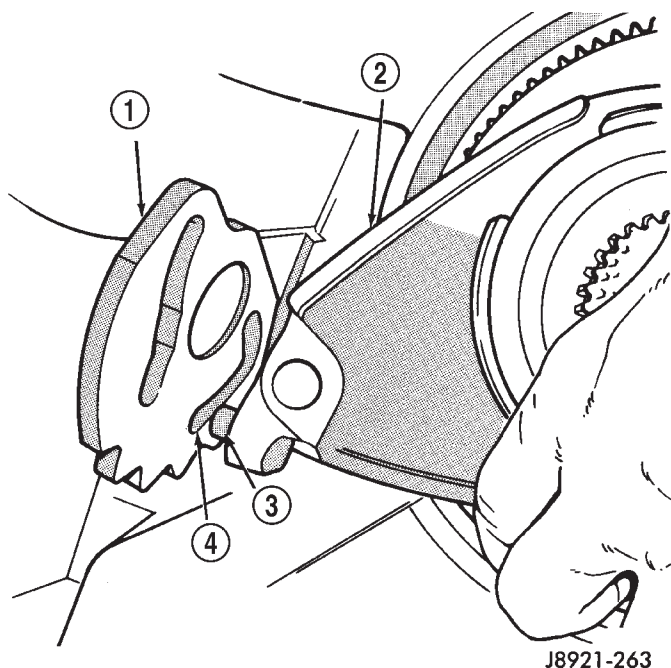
Ensamblaje de la horquilla de baja y la maza
